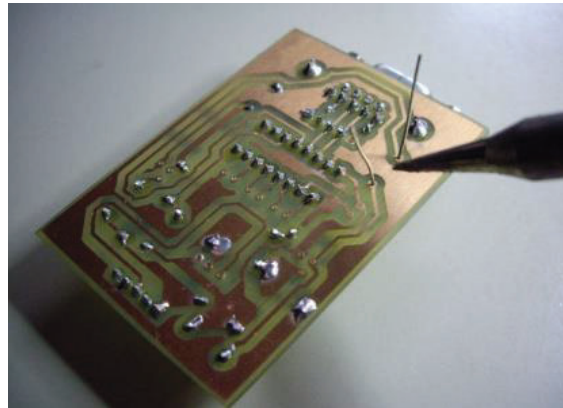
Ubicación y soldadura de los componentes.
